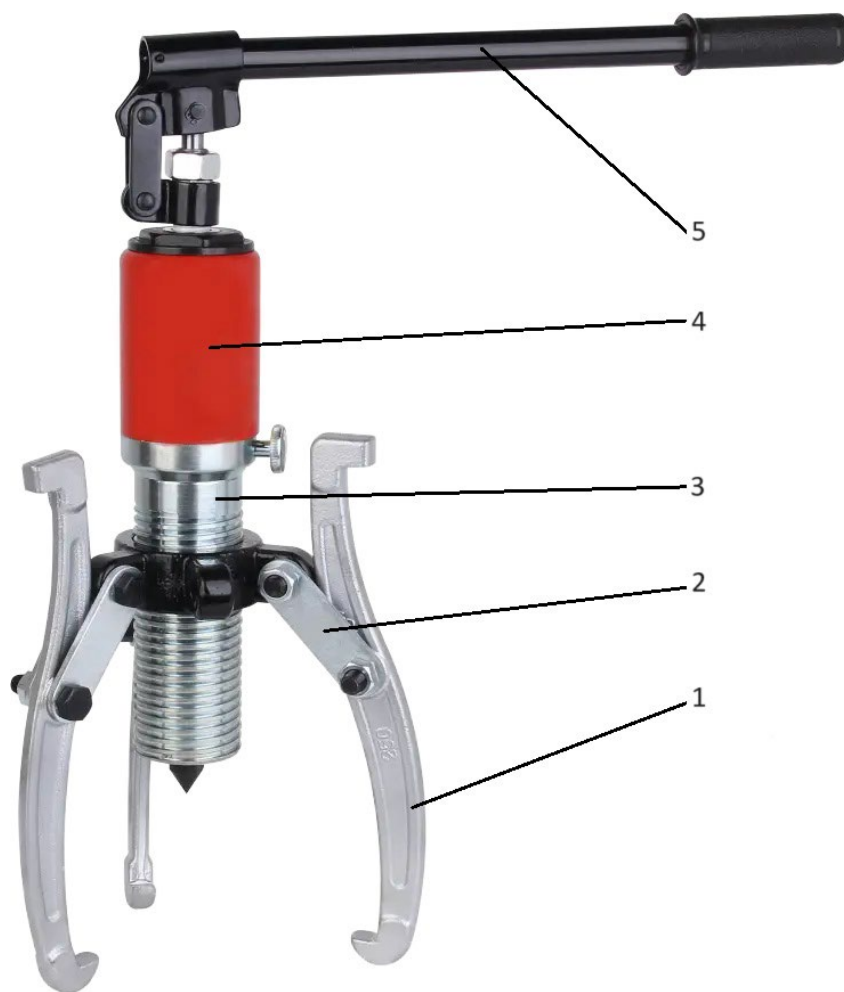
Знімач три захватний 8" редукторний моделі SK23L8R5
